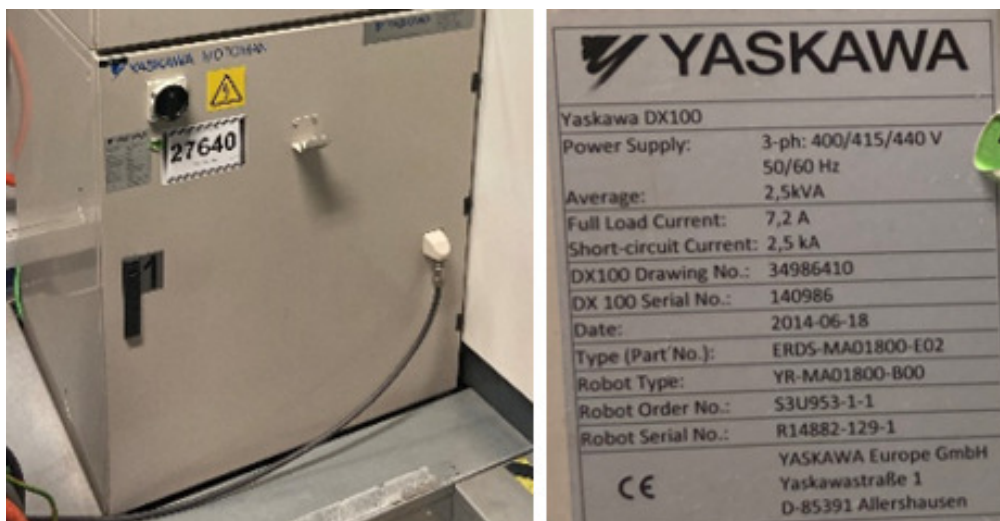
Robô MA1800 com Fonte de Solda SKS e Controlador DX100
